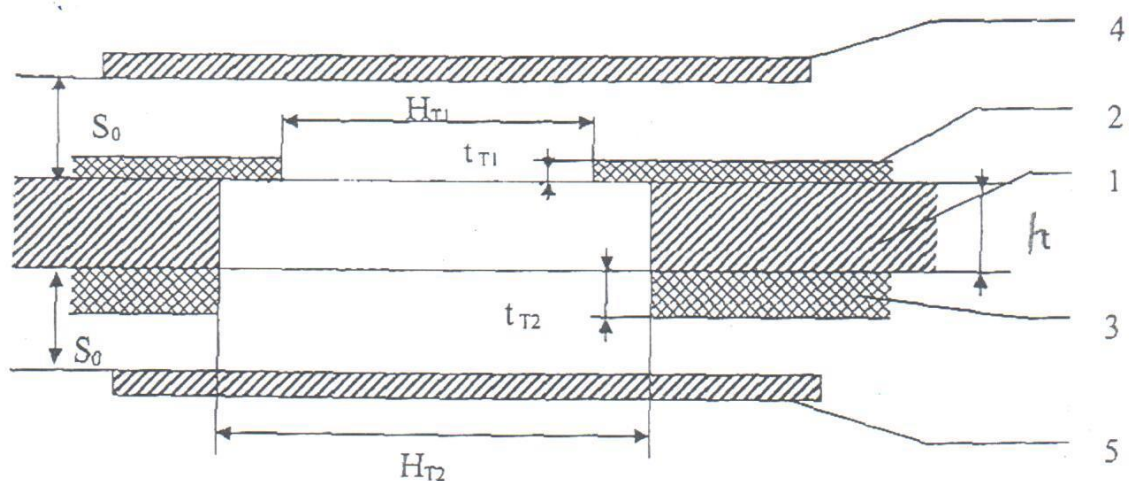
Отверстие в детали после прошивки и калибровки
